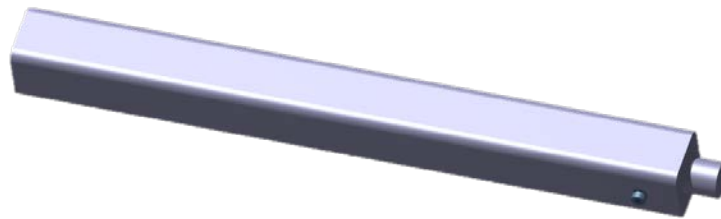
Perfil 60x60x5 y pieza eje de los rodamientos
